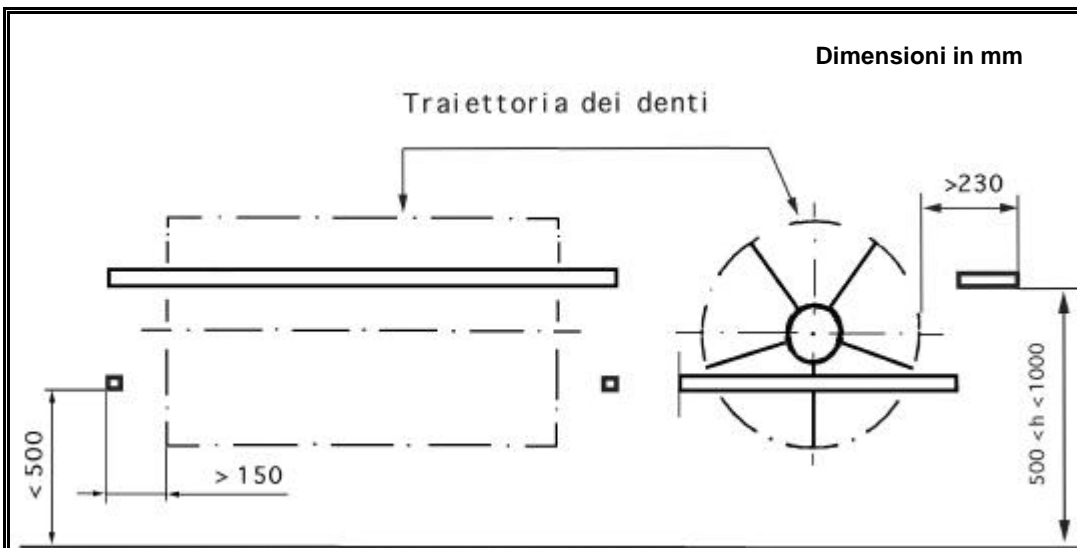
Vista frontale e laterale dei dispositivi di protezione
